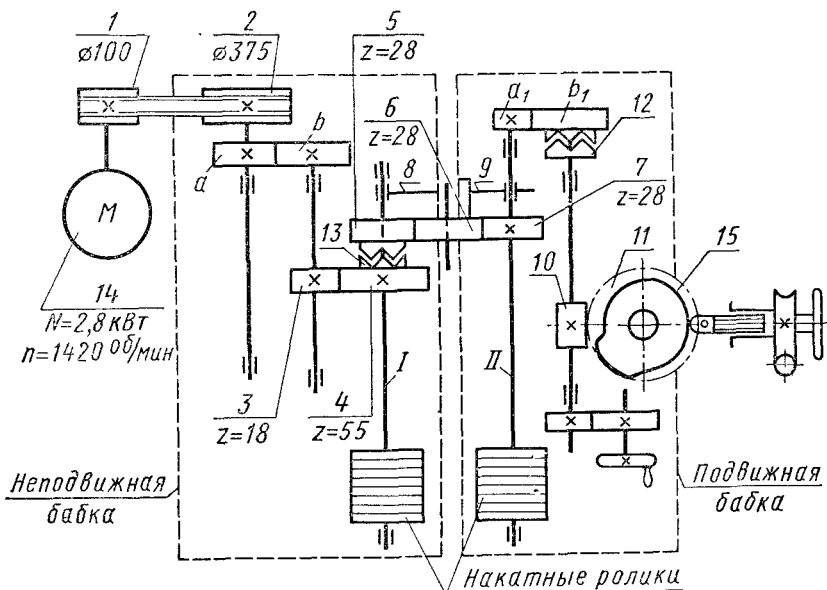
Кинематическая схема резьбонакатного станка мод. 5333
